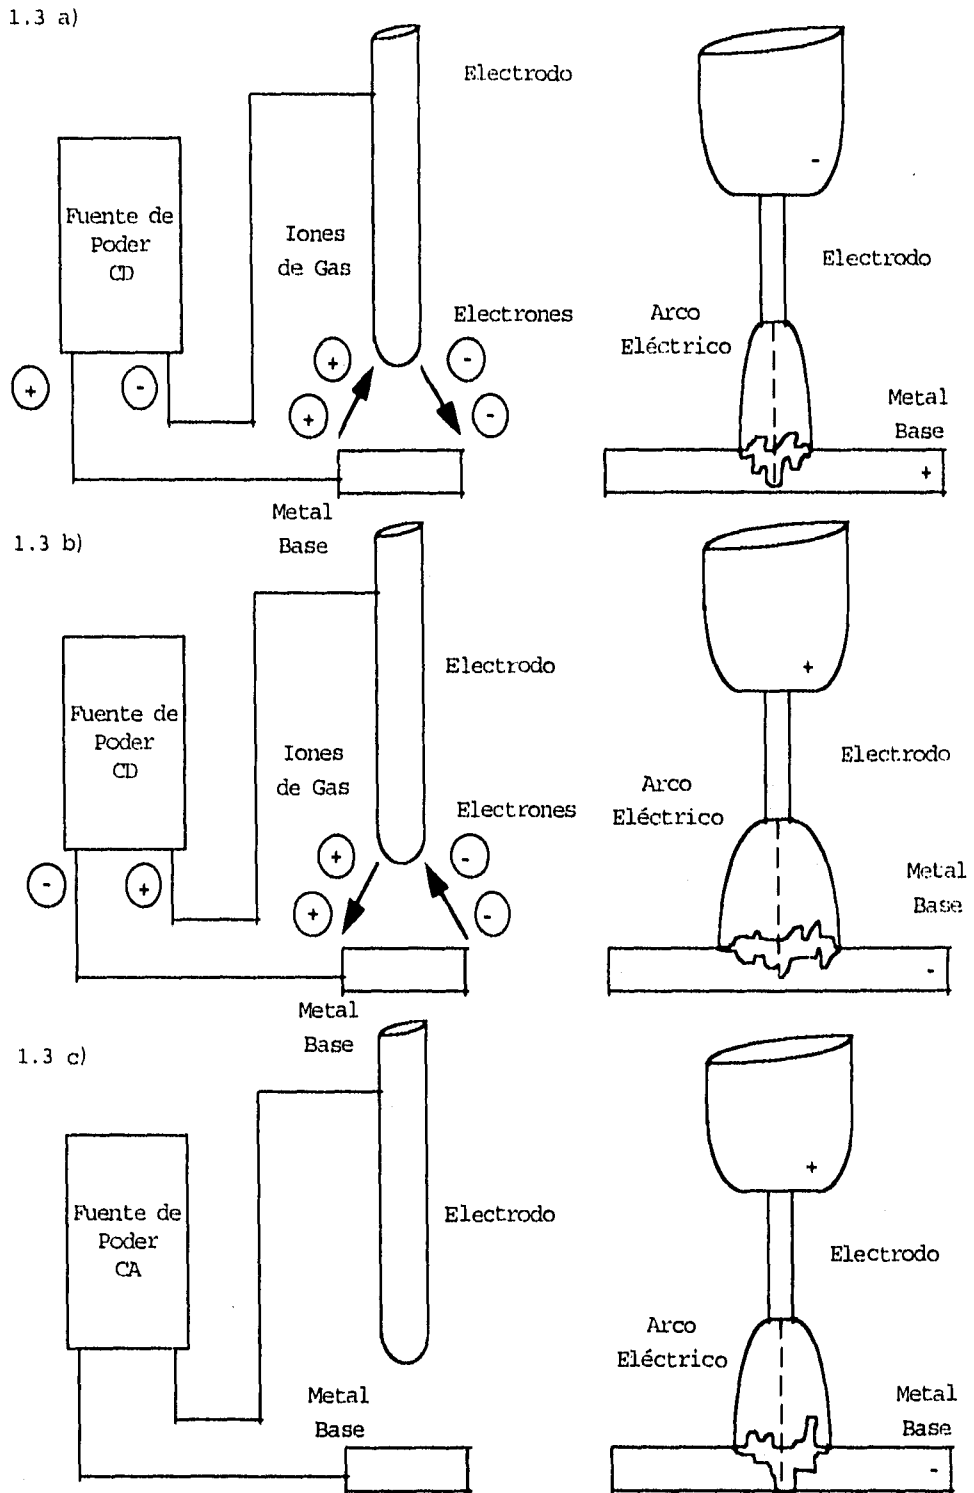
Efectos sobre el proceso de soldadura dependiendo de la manera de conectar el equipo de soldar: a) CD, Polaridad directa, b) CD, Polaridad inversa y c) Corriente alterna.
